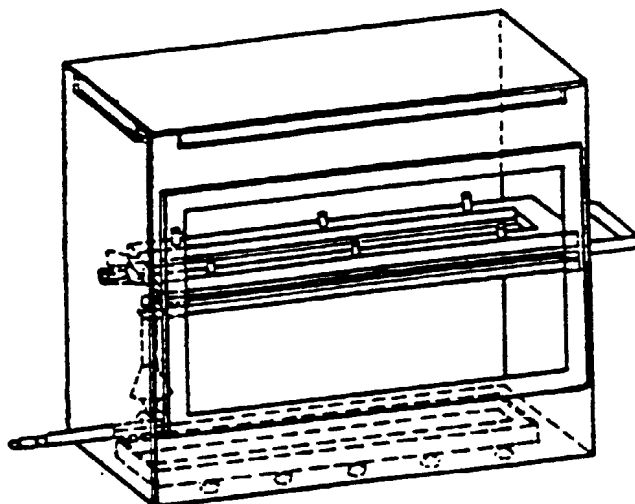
Образец камеры сгорания с подставкой для образца и ванночкой
